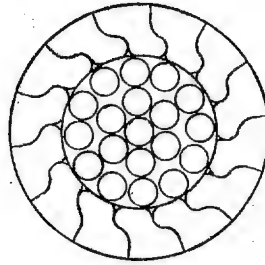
Канаты из круглой и фасонной проволоки (закрытой конструкции)
